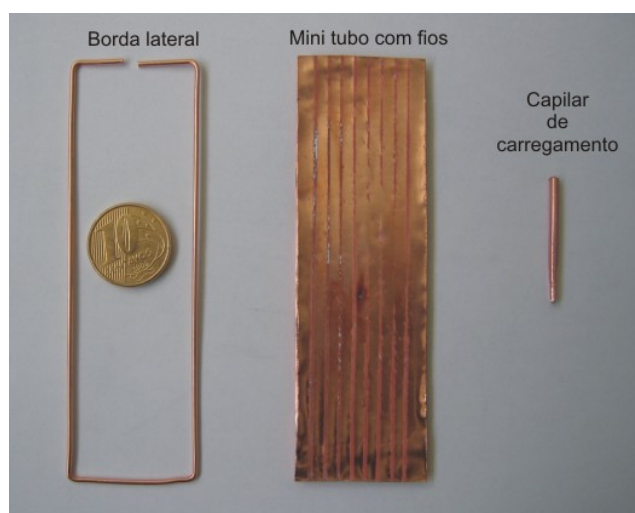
Partes do mini tubo durante o processo de montagem.
